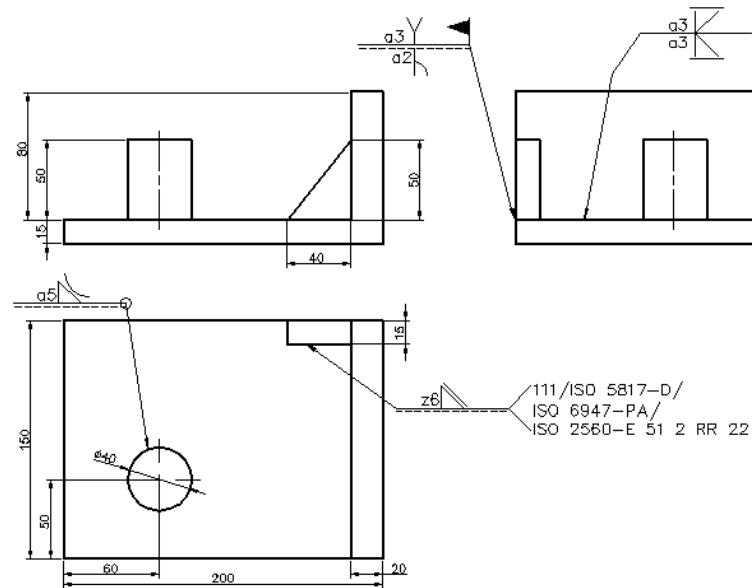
Exemplo de Representação da Juntas Soldadas
